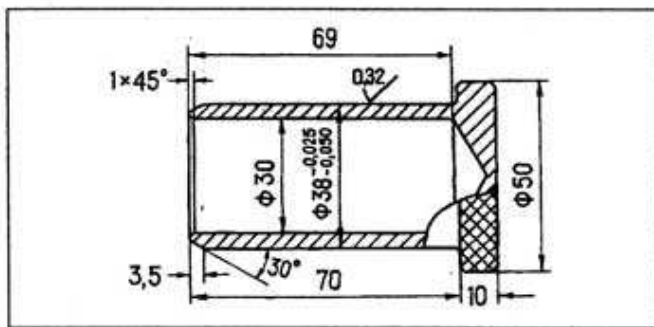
Пробка-заглушка в удлинителе коробки передач
